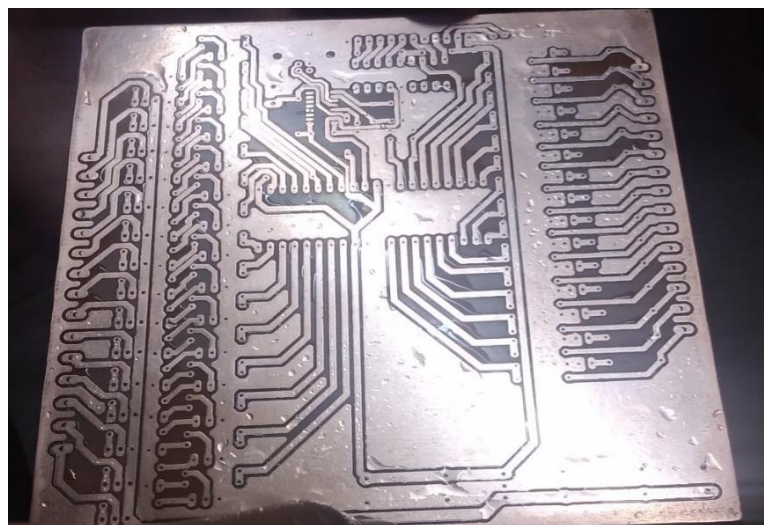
Desarrollo del circuito impreso en la placa PCB
